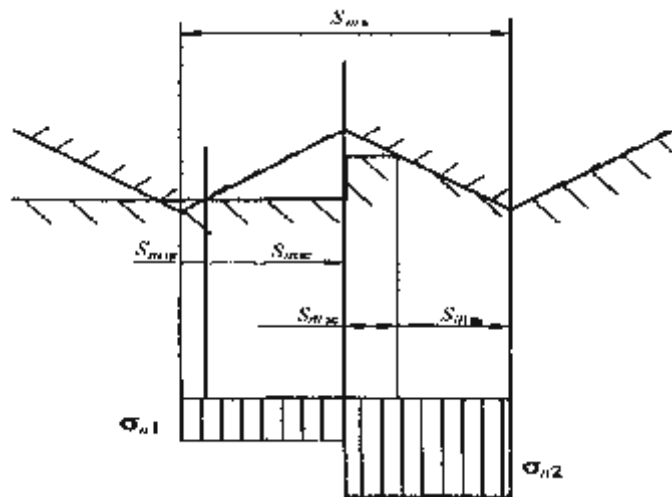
Вдавливание шероховатой поверхности валка в замороженную корку металла
